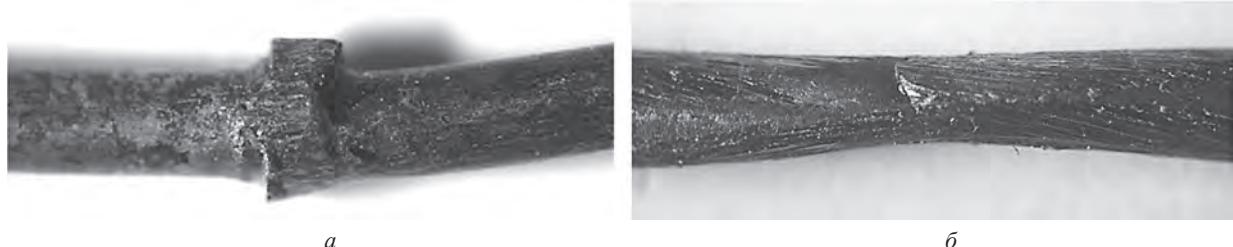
Внешний вид сварного шва на проволоке с дефектом «несоответствие диаметра»: *а* – превышение диаметра сварного соединения; *б* – переточка диаметра сварного соединения
